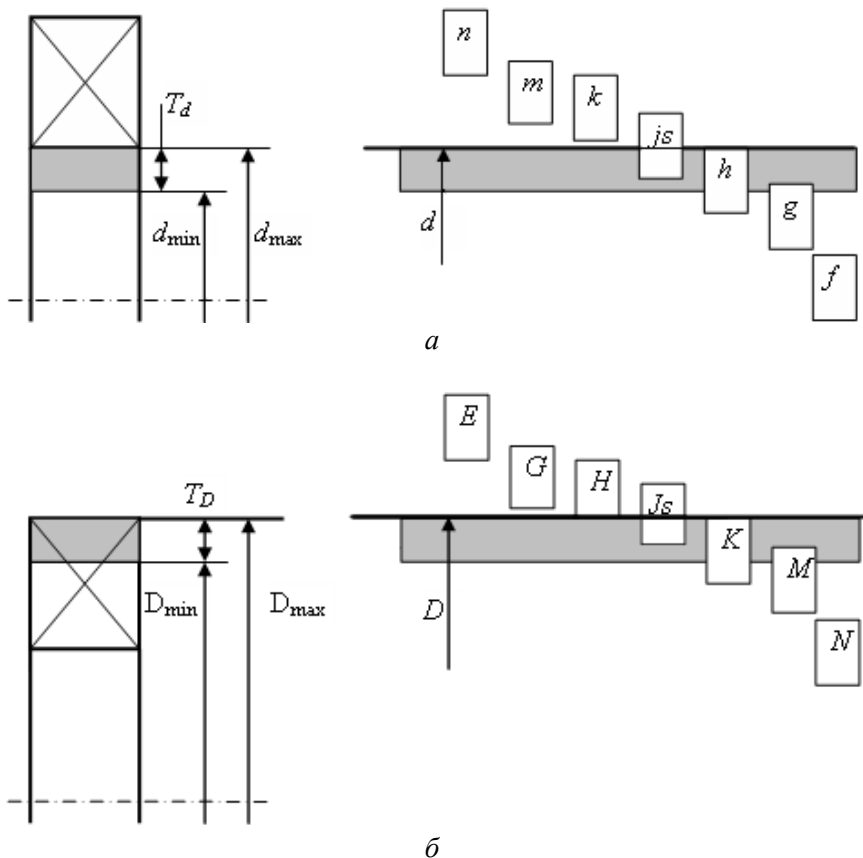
Схемы расположения полей допусков колец подшипников со стандартными полями допусков валов и корпусов:
